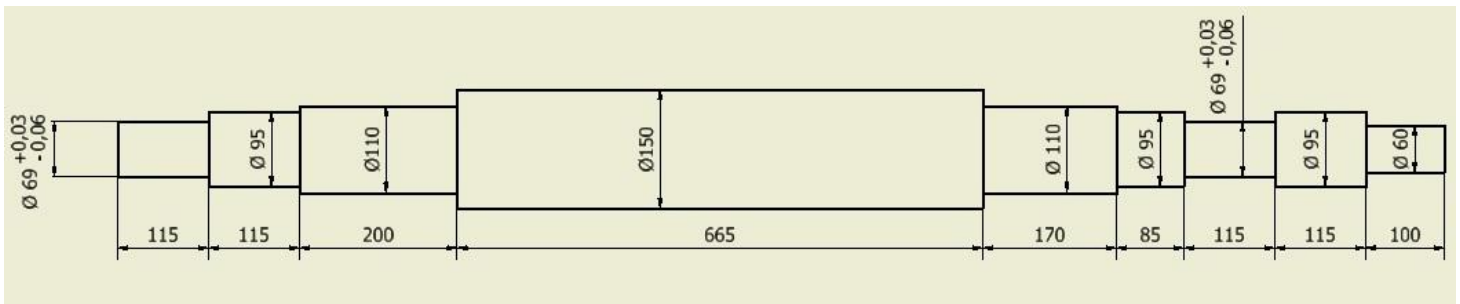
Dimensiones y tolerancias del árbol rediseñado.
